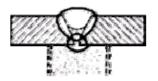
Соединение стыковое со скосом кромок двустороннее с предварительной подваркой корня шва С 21
